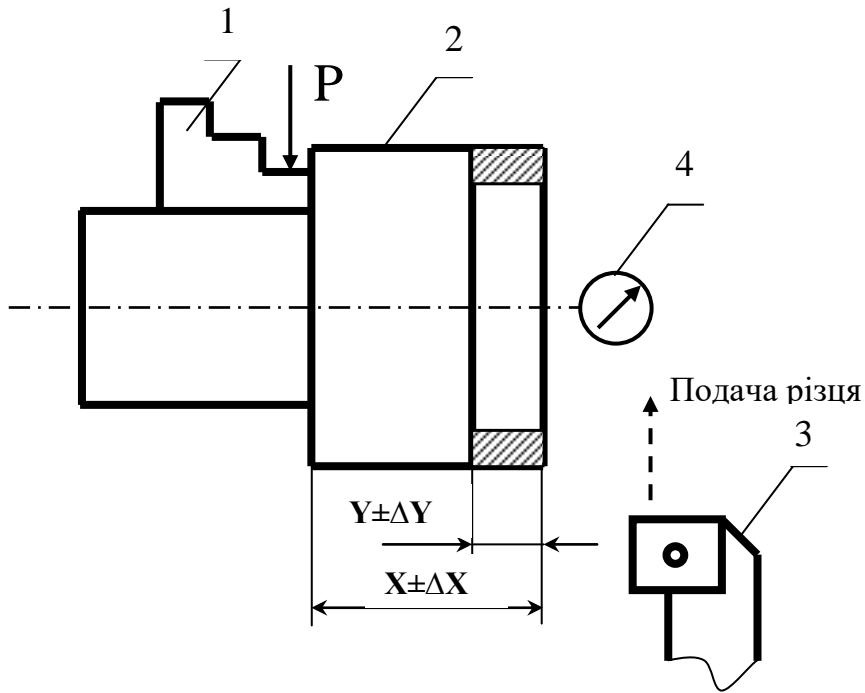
Схема виміру погрішності установки деталі в патроні токарного верстата
